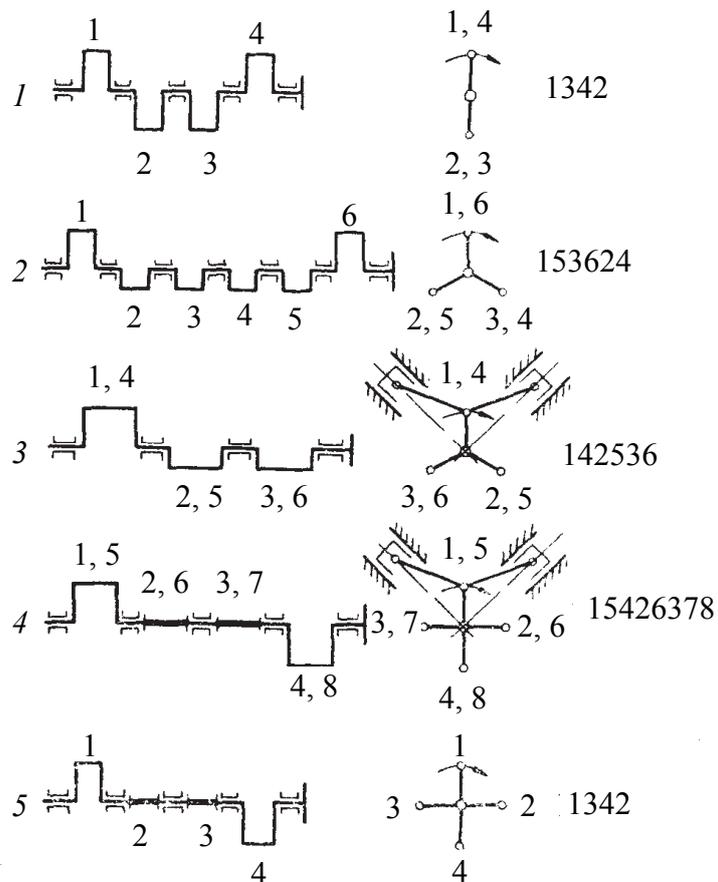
Схемы коленчатых валов и порядок работы двигателей:
